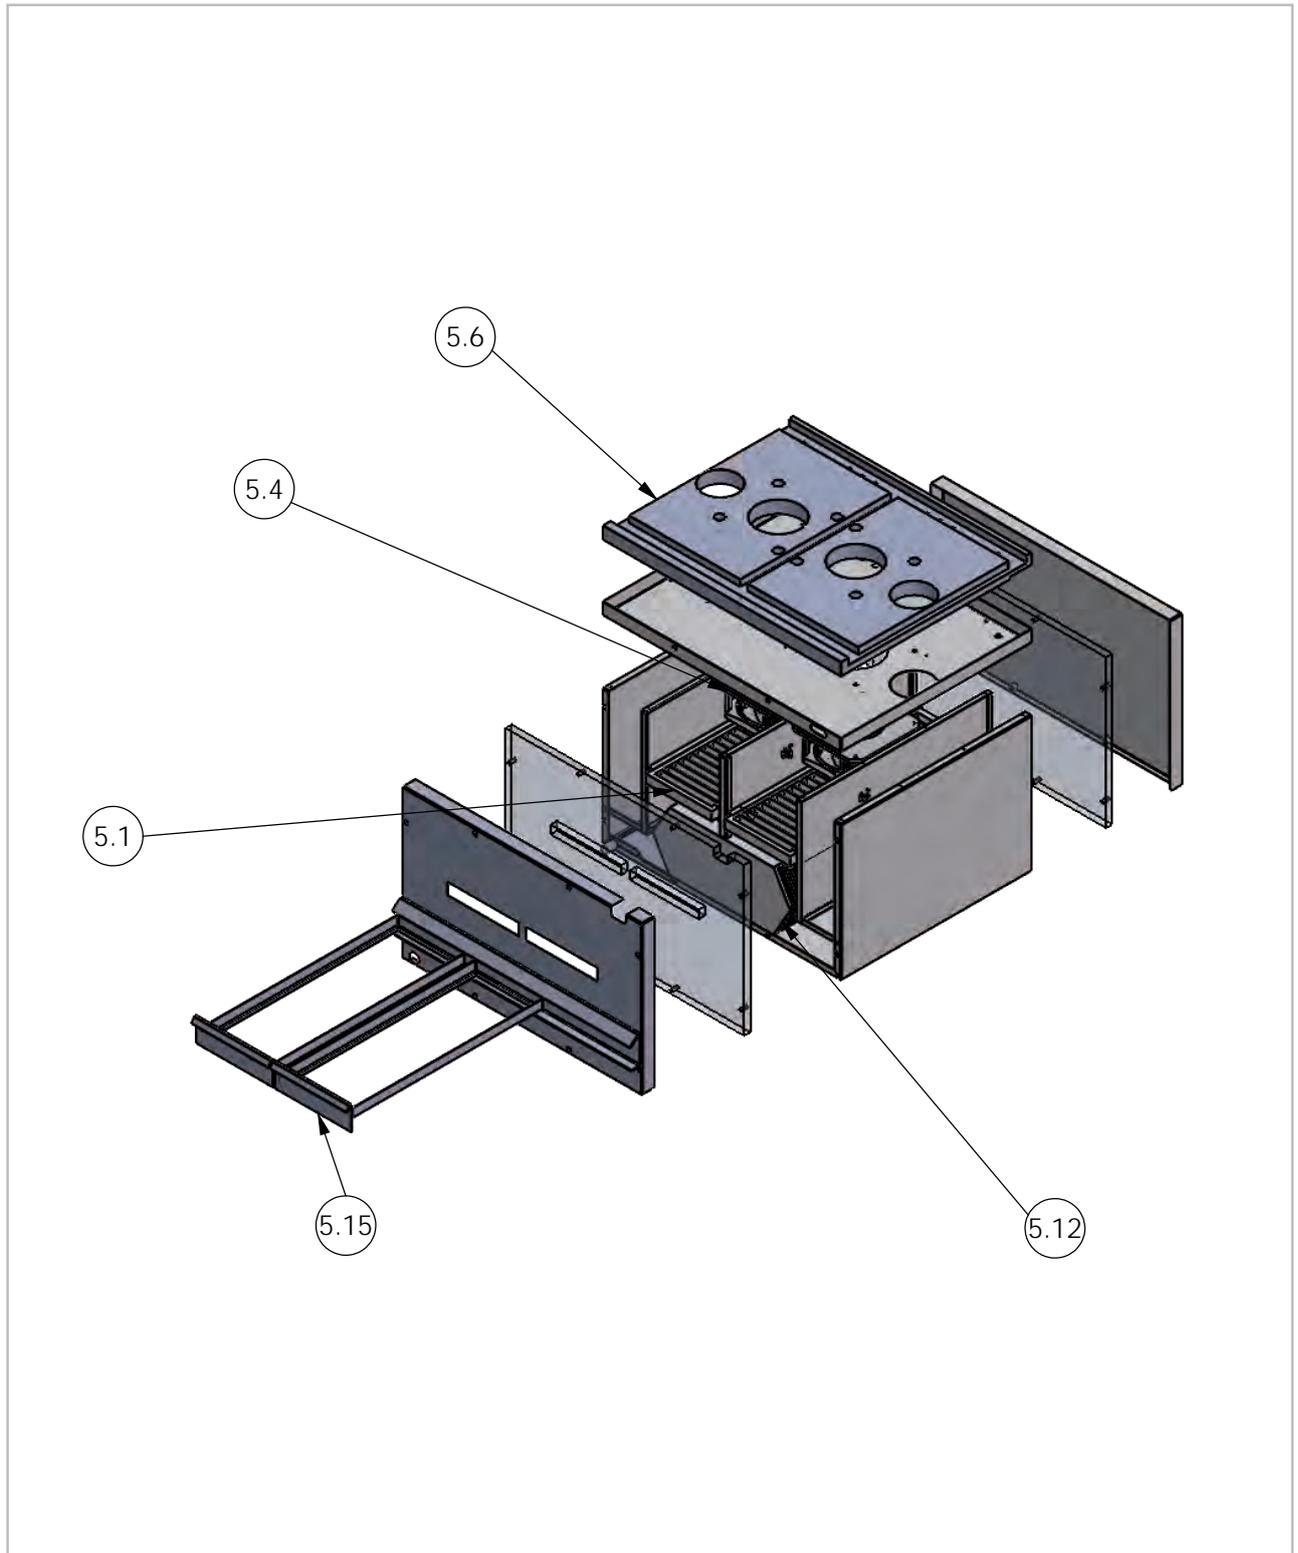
Explosionszeichnung Lüftungsmodul MLG 70
